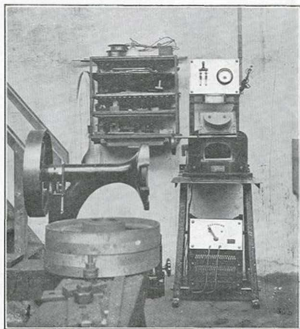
Four Deliot et Cheminat de 3 kW, utilisé pour la trempe et le revenu des différentes pièces des machines àagrafer.
